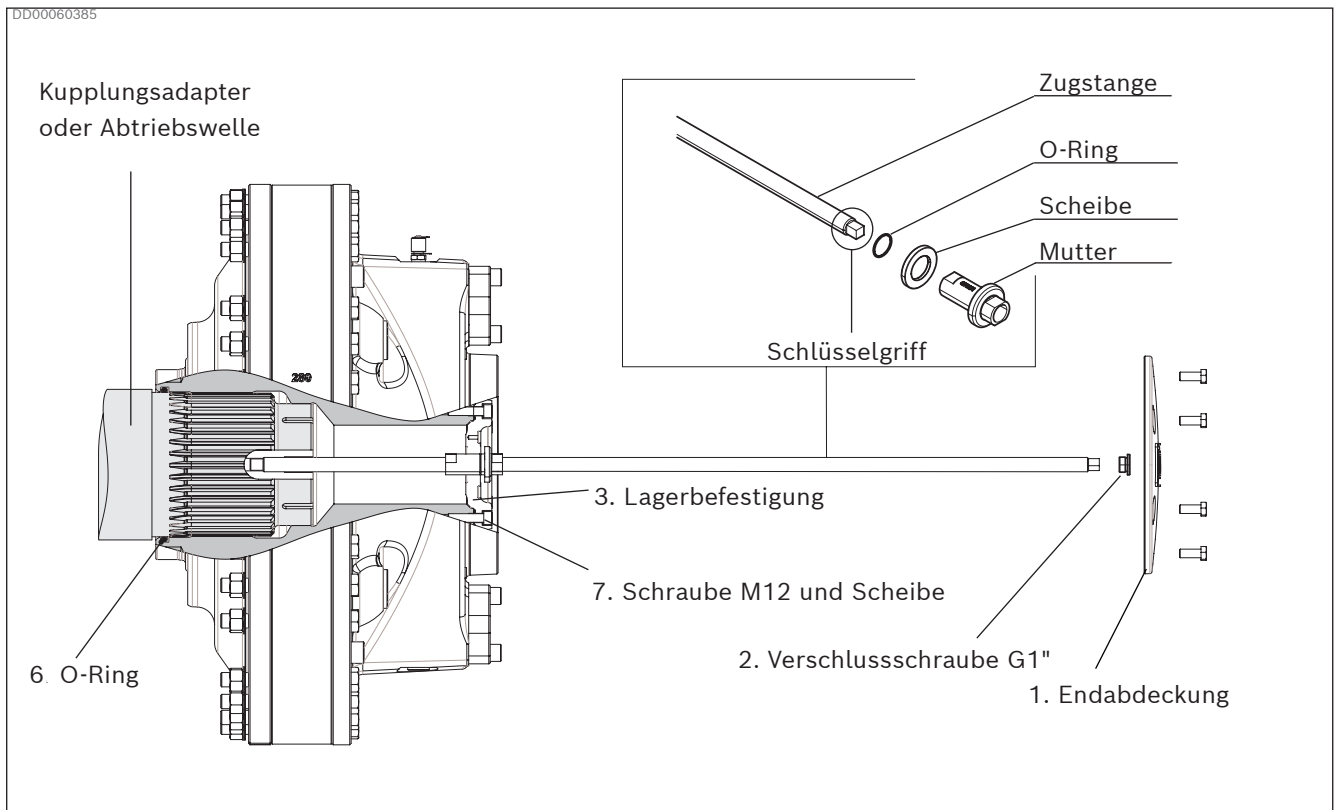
Montage des Motors mit Vielkeilnut mithilfe des Montagewerkzeuges
